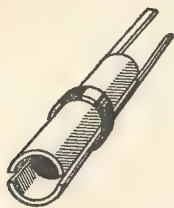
Zum Einbau fertiger Plattensatz, bestehend aus zwei halbrunden Platten, die durch zwei Holzpflocke voneinander getrennt sind und durch den Gummiring zusammengehalten werden.
